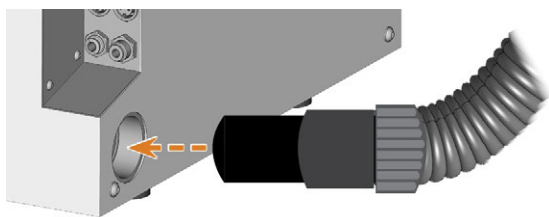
INSERIMENTO DELLA CONNESSIONE DEL TUBO NELL'APERTURA DEL SISTEMA DI ESTRAZIONE DELL'ARIA
